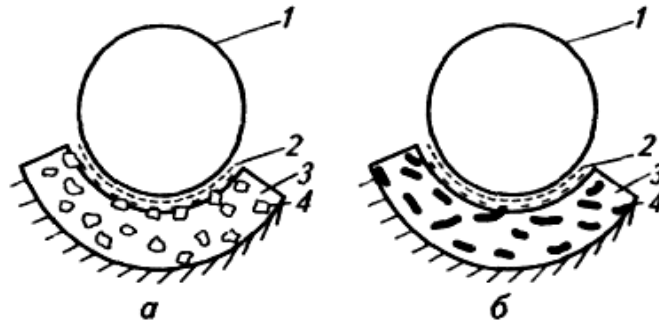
Узлы трения скольжения с различными антифрикционными сплавами: *а* – с твердыми включениями; *б* - с мягкими включениями; 1 - вал; 2 - смазочный материал; 3 - основа; 4 - включения
